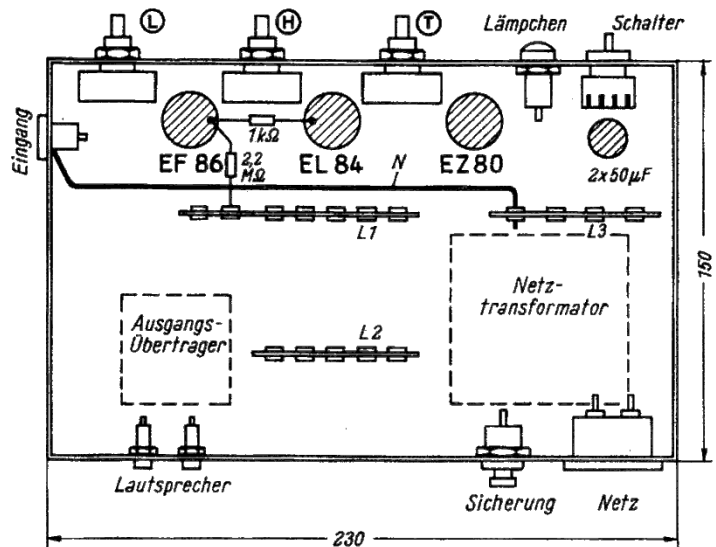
Chassis-Ansicht von unten. Die Chassis-Tiefe beträgt 60 mm
